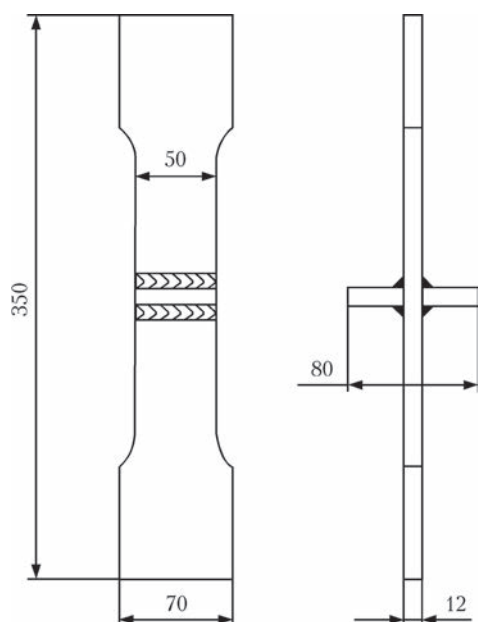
Форма и геометрические размеры образца таврового сварного соединения
